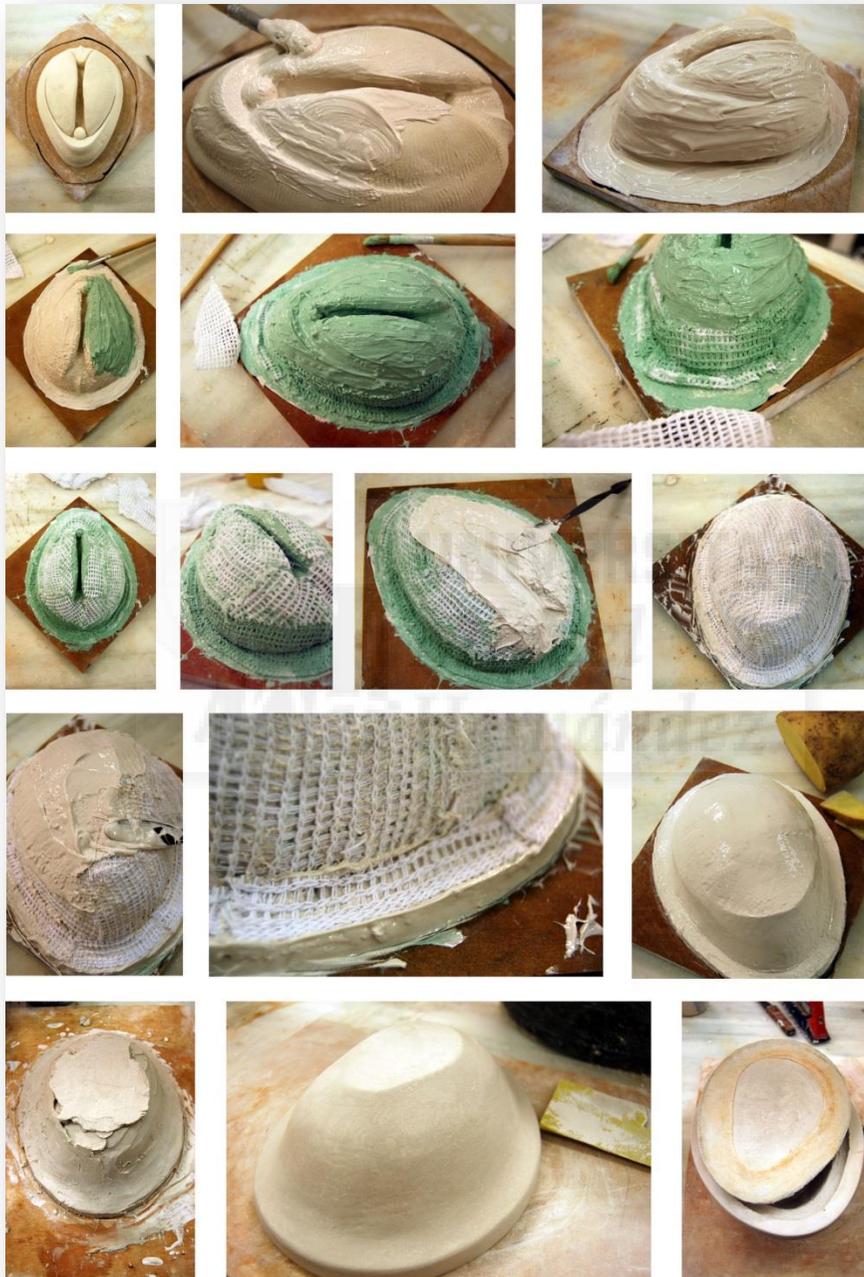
Molde reutilizable flexible de un fragmento por estampado.
